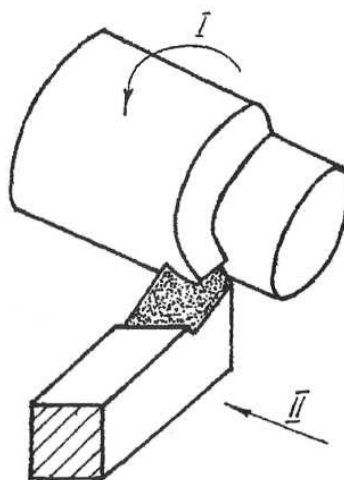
Основные движения при токарной обработке. I - главное; II - движение подачи.
